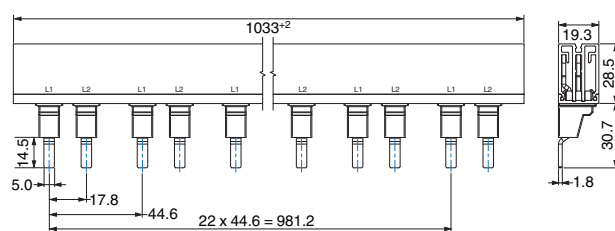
Dimensions de TMC 8...B2...CA (mm)
